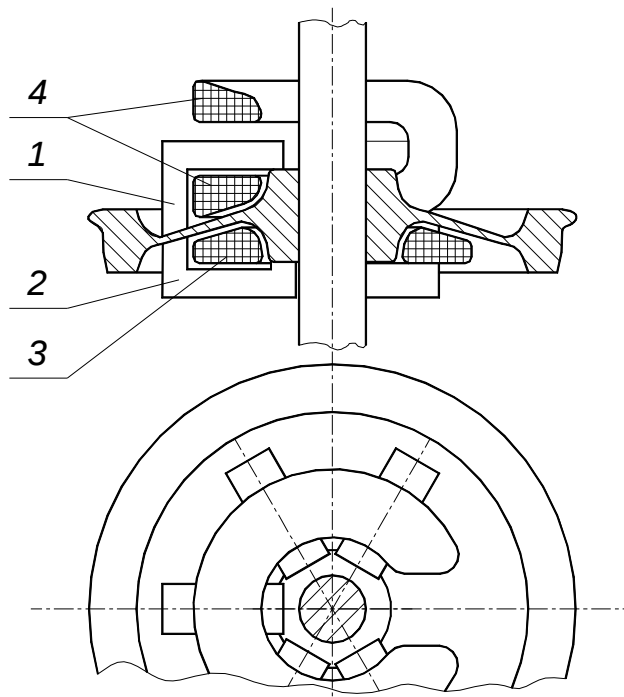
Индуктор для нагрева под разборку колесной пары тепловоза:
